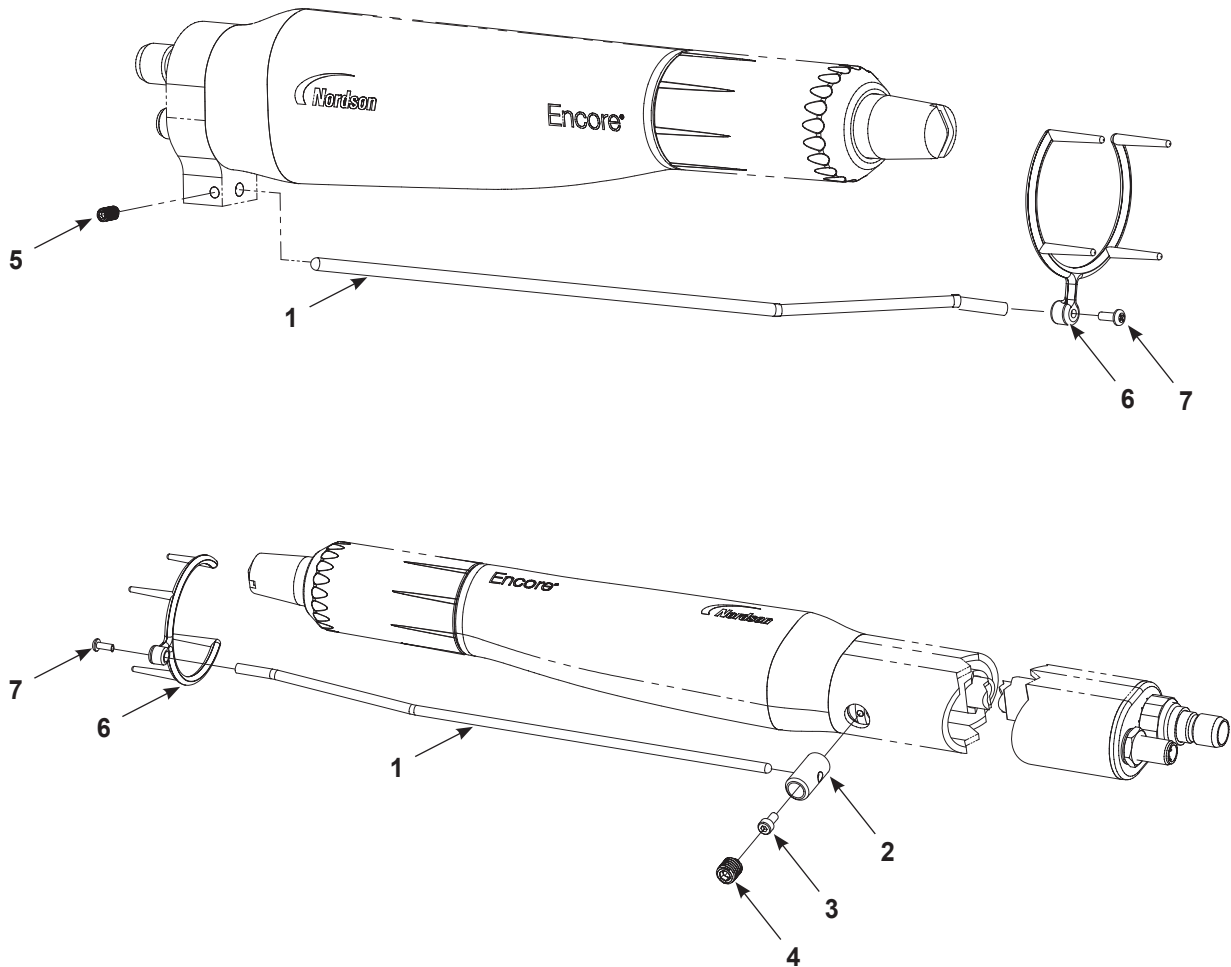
Tyč pistole pro pistole upevněné na tyči
